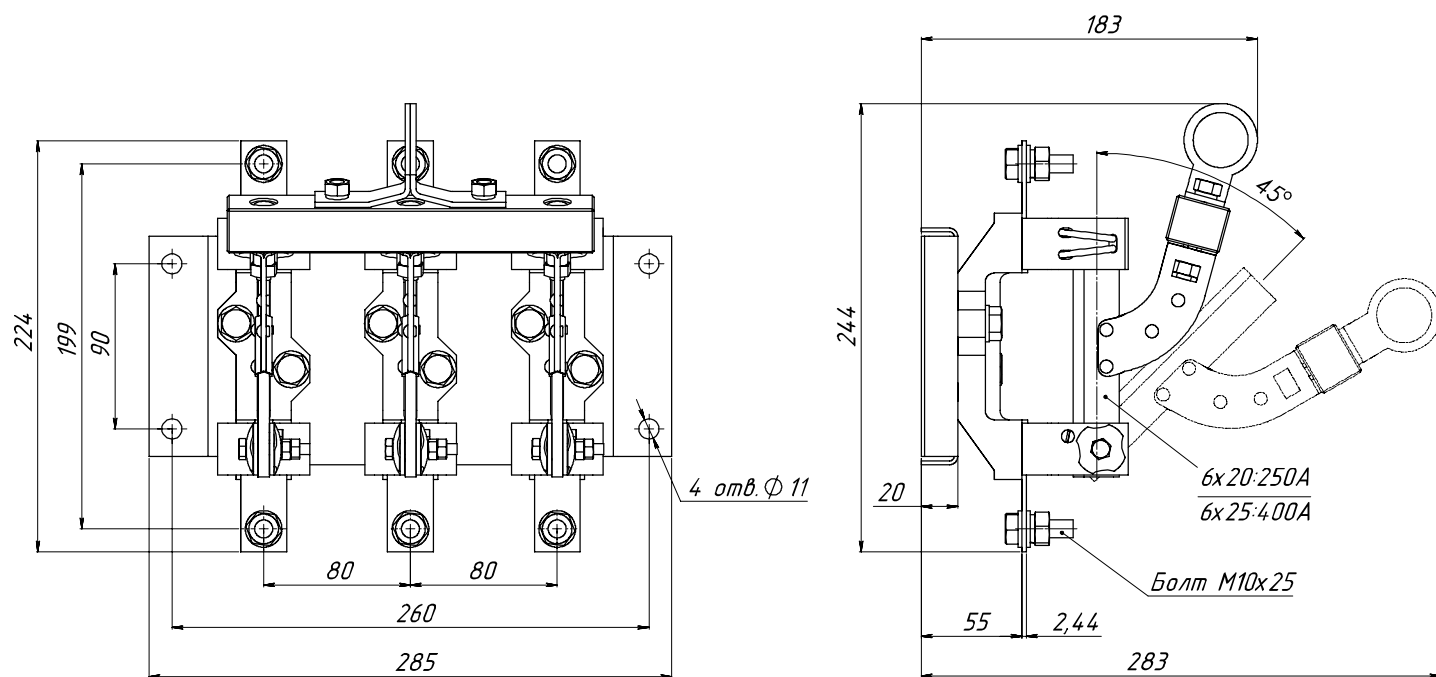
Разъединитель PE19 трехполюсный с центральной штангой, переднего присоединения шин
